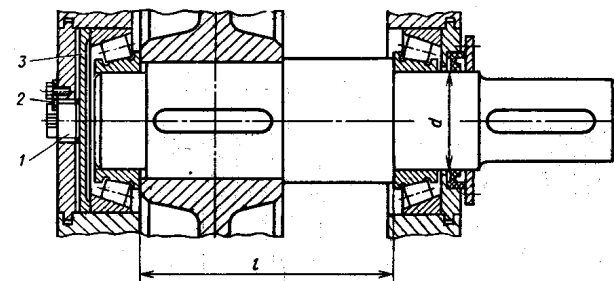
Вал установлен на конических роликоподшипниках; крышки врезные
